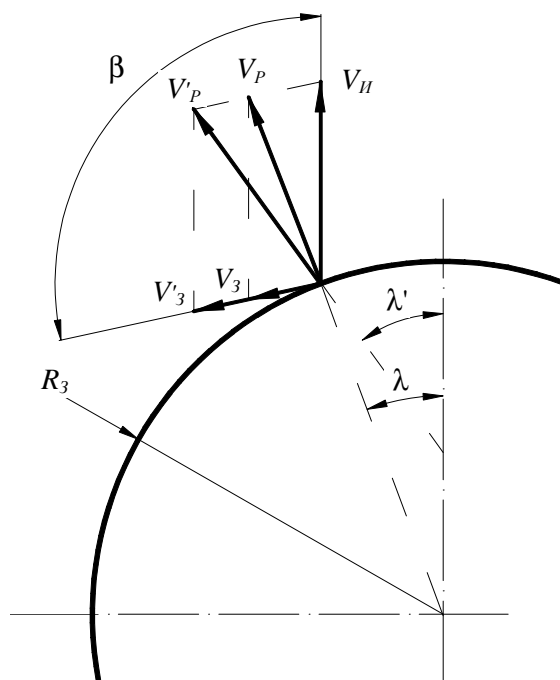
Направление скоростей движений при обработке торцовых зубчатых контуров
